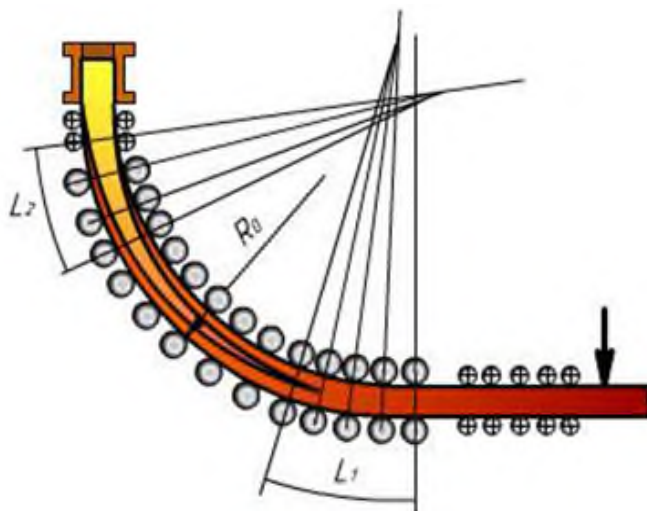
Схема МБЛЗ криволінійного типу (L_1 – участок разгиба заготовки; L_2 – участок загиба заготовки; R_0 – базовий радіус МБЛЗ)
